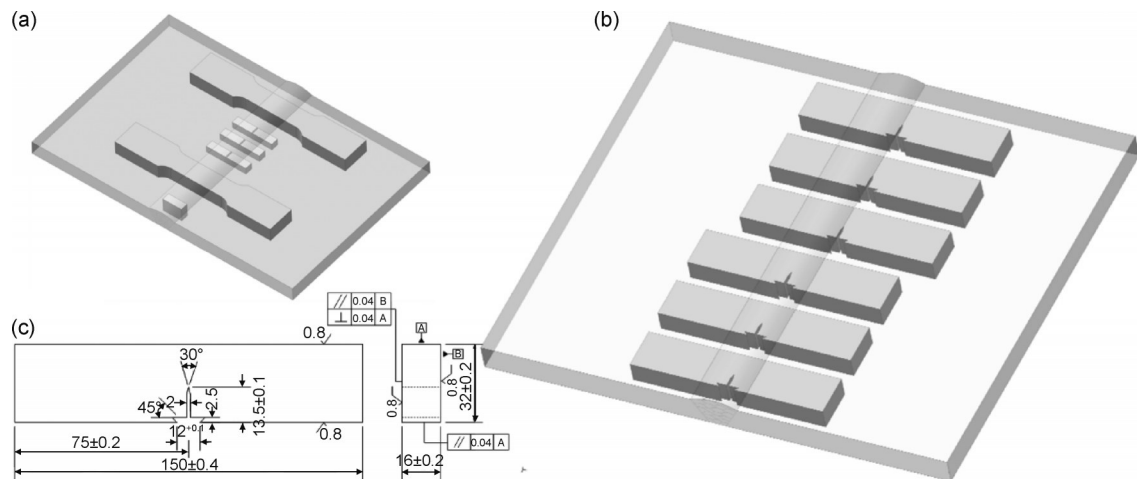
试板焊接后力学性能检测试样取样位置及断裂韧性试样尺寸
